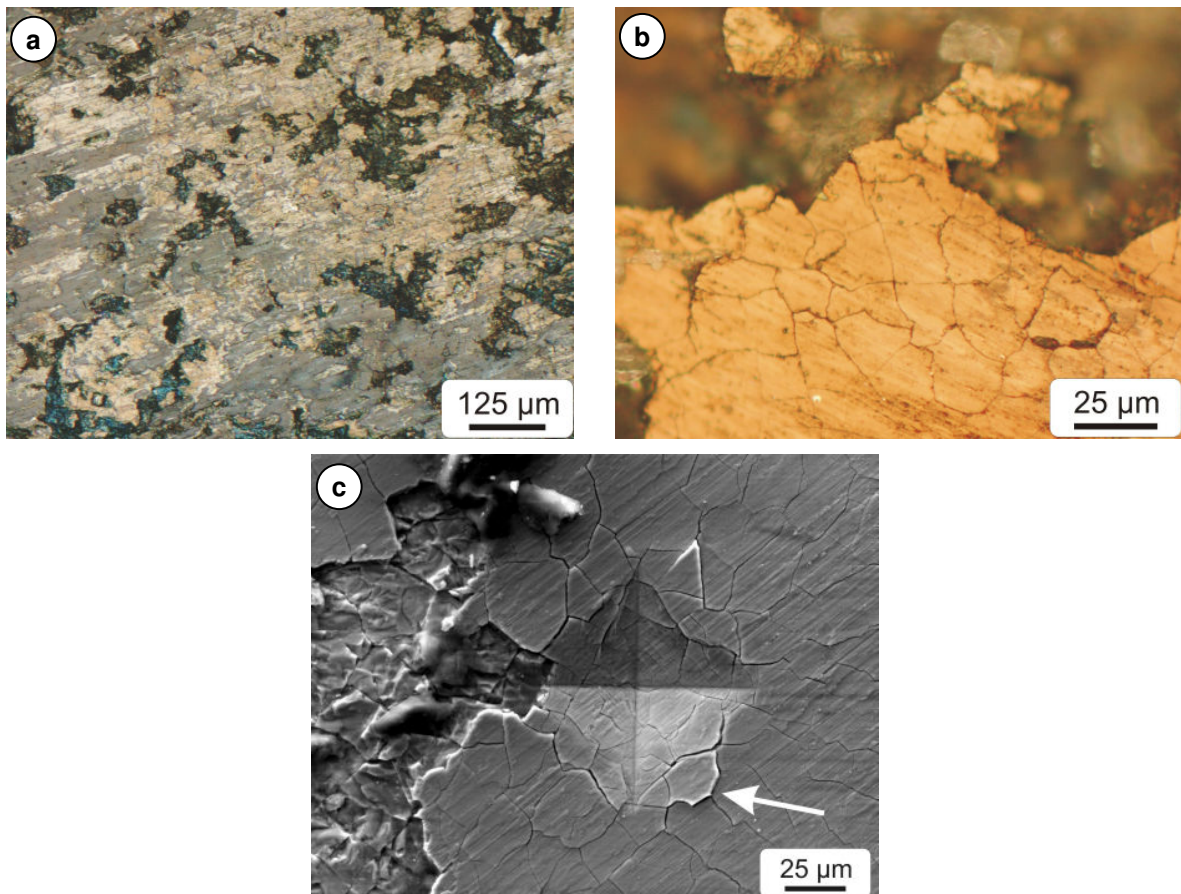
Aufsicht auf Oberflächen des lösungsgeglühten Gefüges nach Bearbeitung mit 4000 m/min
